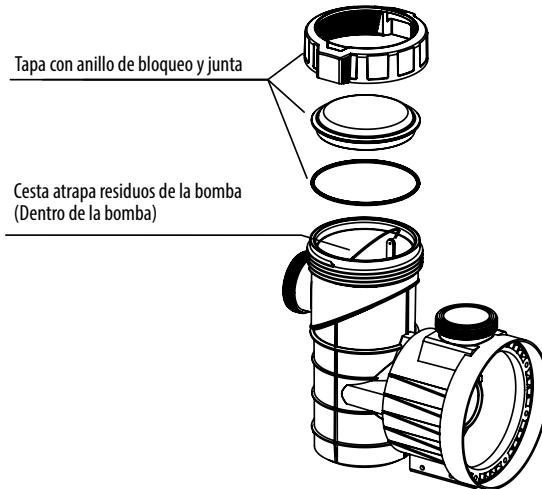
PLANO DE DESPIECE CONJUNTO CUERPO BOMBA
